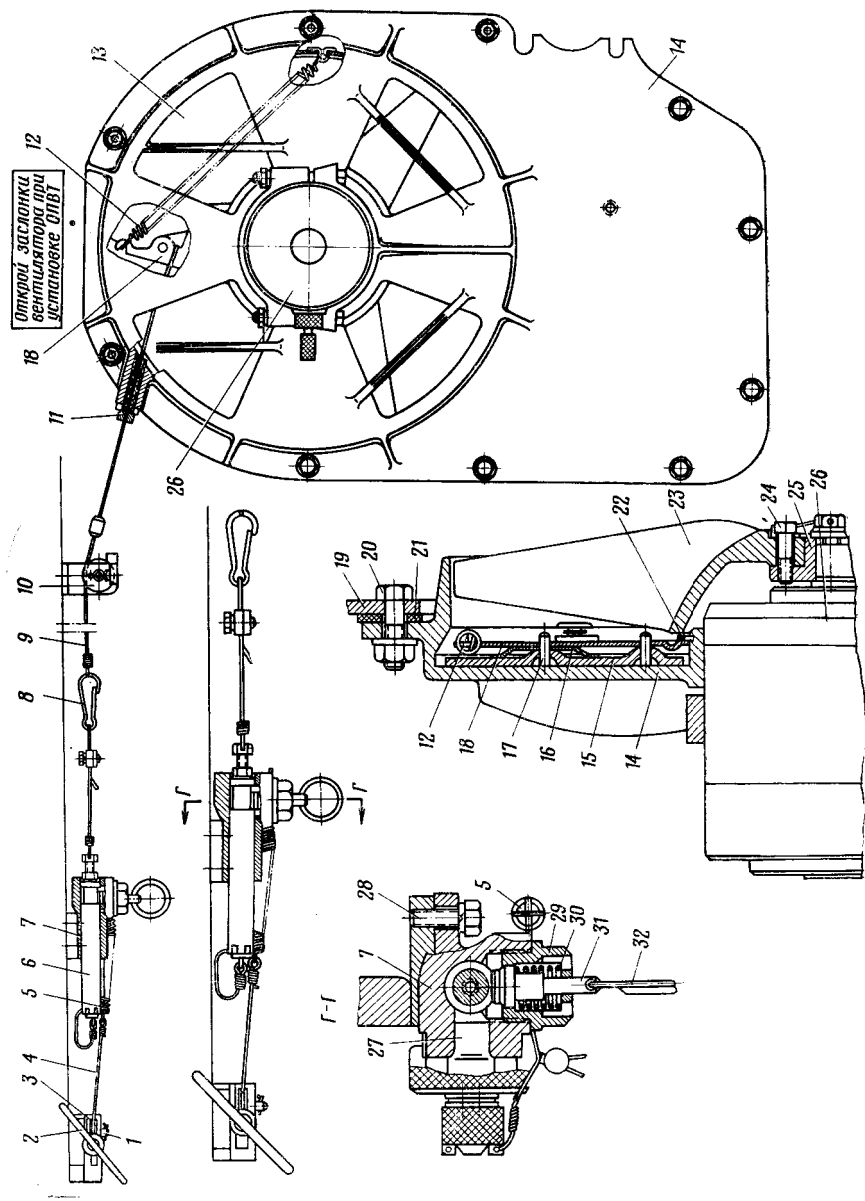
Механизм закрывания окон вытяжного вентилятора:
